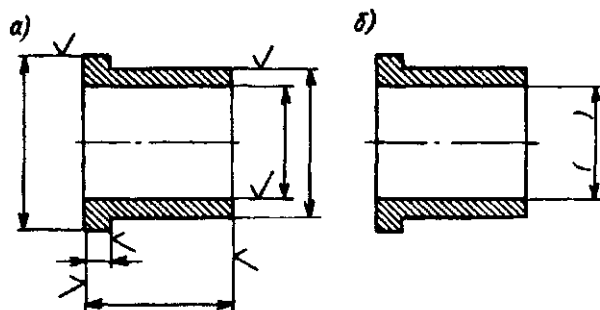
Нанесение размеров и шероховатости поверхности детали: *а* — готовой к сборке; *б* — обрабатываемой в процессе сборки
